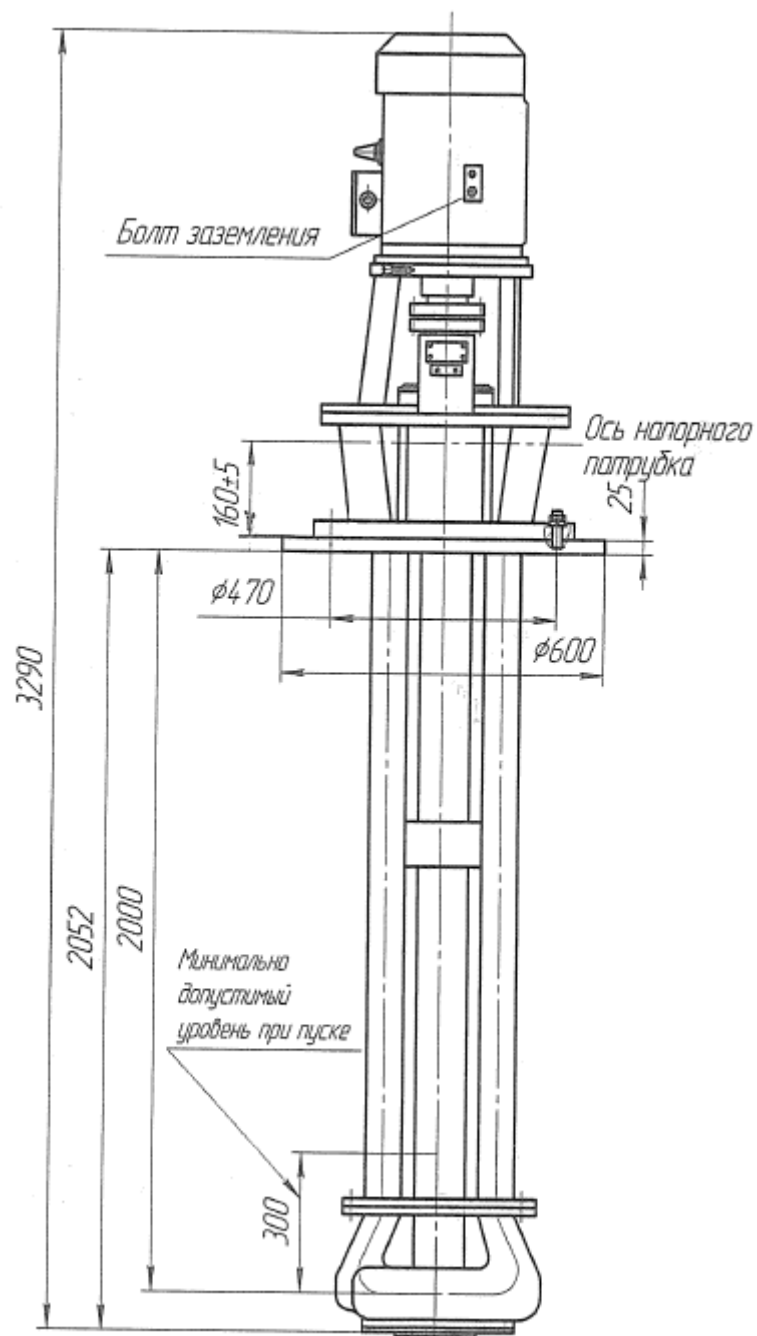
Габаритный чертеж насоса дренажного бака типа ХП45/54-2,0-Щ
